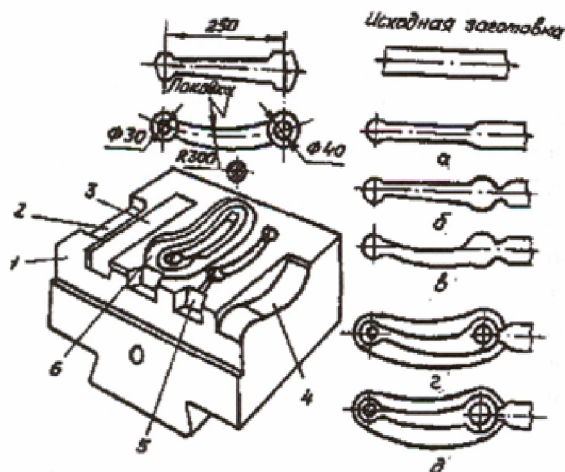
Многоручьевого штамп: 1 – штамп, 2 – протяжной ручей, 3 – подкатной, 4 – гибочный, 5 – предварительный, 6 – окончательный; переходы: а – протяжка, б – подкатка, в – гибка, г, д – предварительная и окончательная штамповка
